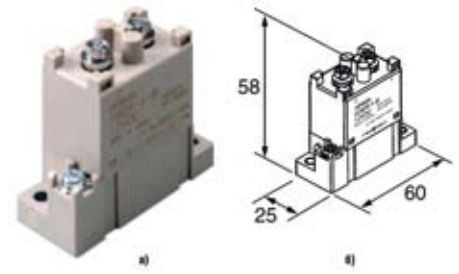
Внешний вид и габаритные размеры реле G9EB
